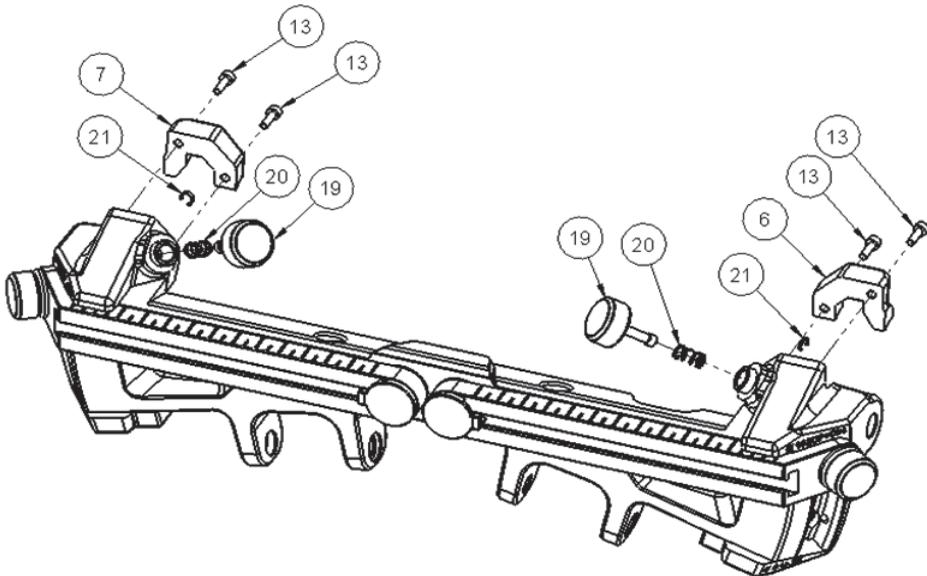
Vista esplosa del gruppo frontale: 2° parte
